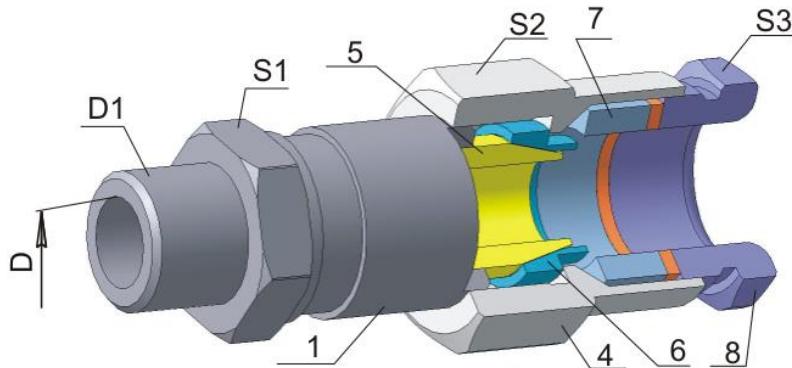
Конструкция кабельного ввода для монтажа бронированного кабеля
